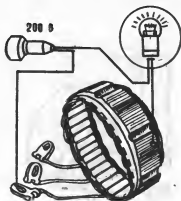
Проверка обмотки статора на замыкание с корпусом.
